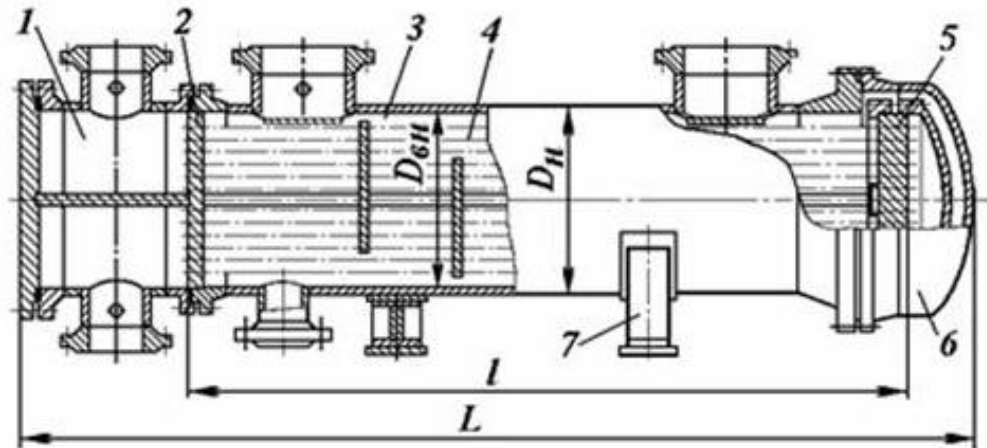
Кожухотрубний горизонтальний багатходовий конденсатор з плаваючою головкою (КП) з роз'ємною камерою і плоским днищем; 1 - камера розподільна; 2 - трубна решітка; 3 - корпус; 4 - трубчатка; 5 - плаваюча голівка; 6 - кришка; 7 - опора.
